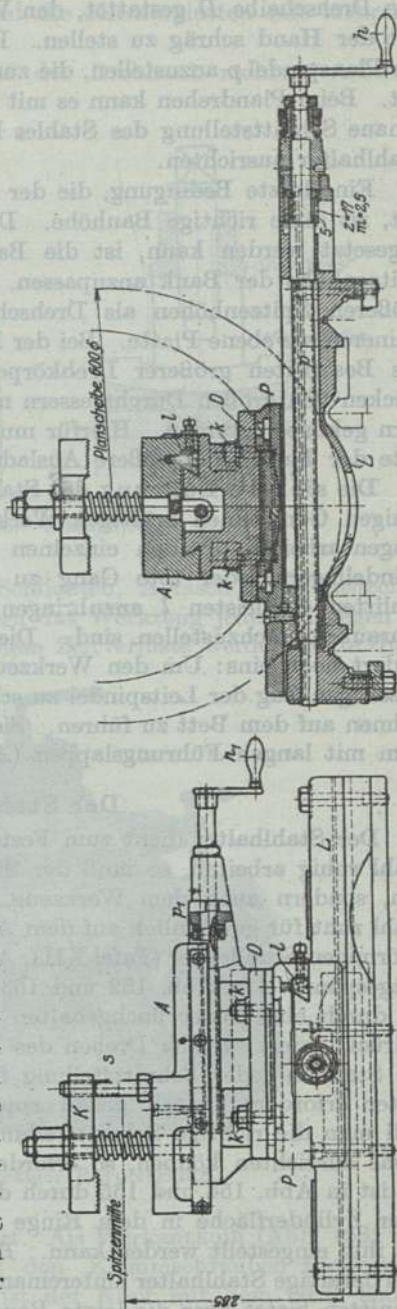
und 153. Magaburger Werkzeugschlitten, 255 mm Spitzenhöhe.
